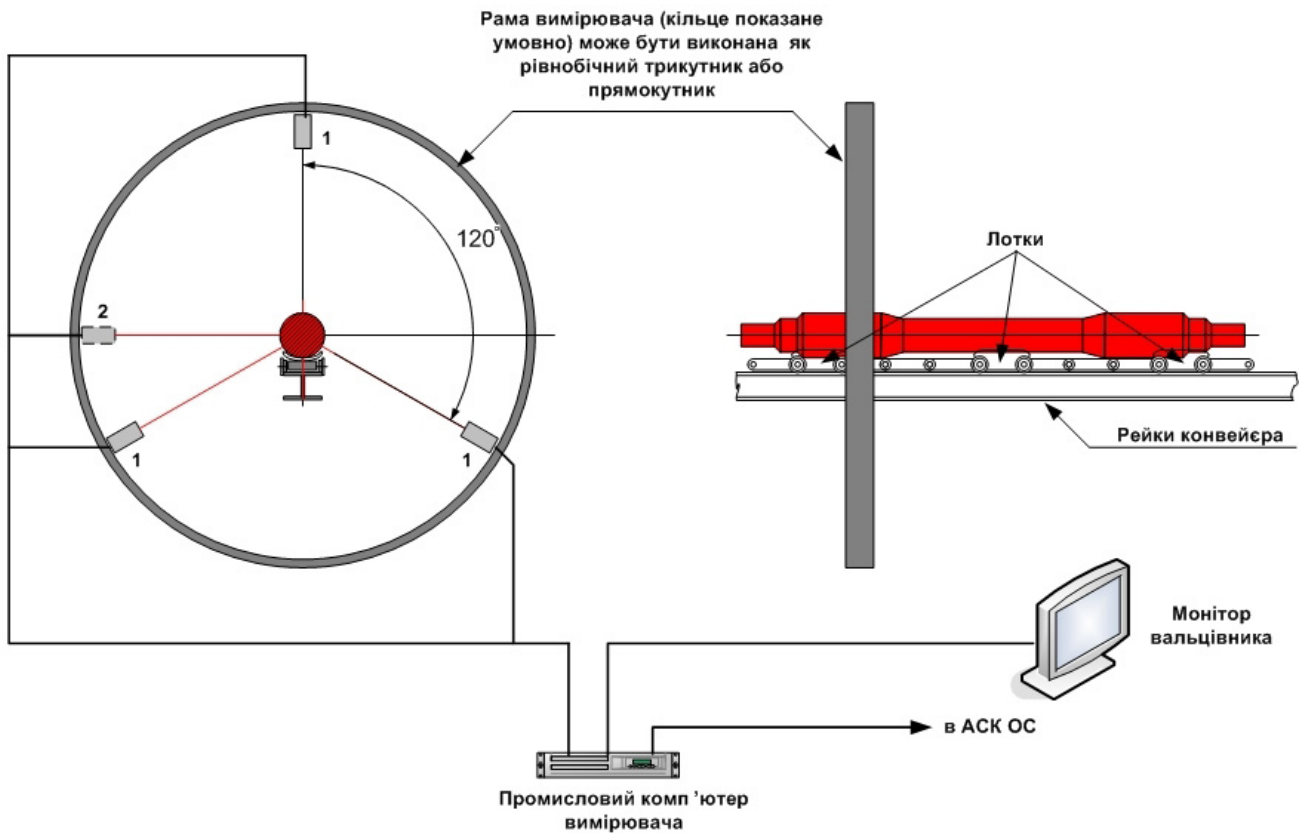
Схема вимірювання геометричних розмірів осевої заготовки:
